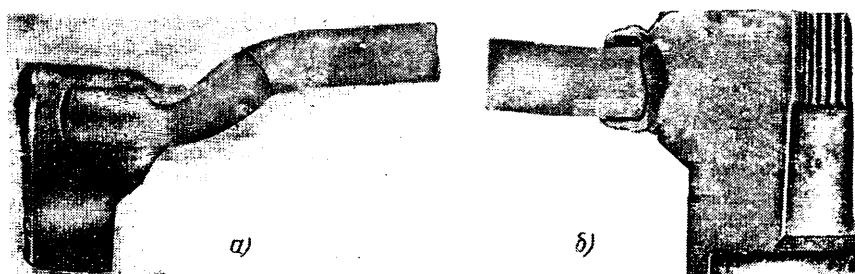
Виды разрушения после испытания на усталостную прочность сварных соединений каркаса рулевого колеса:
